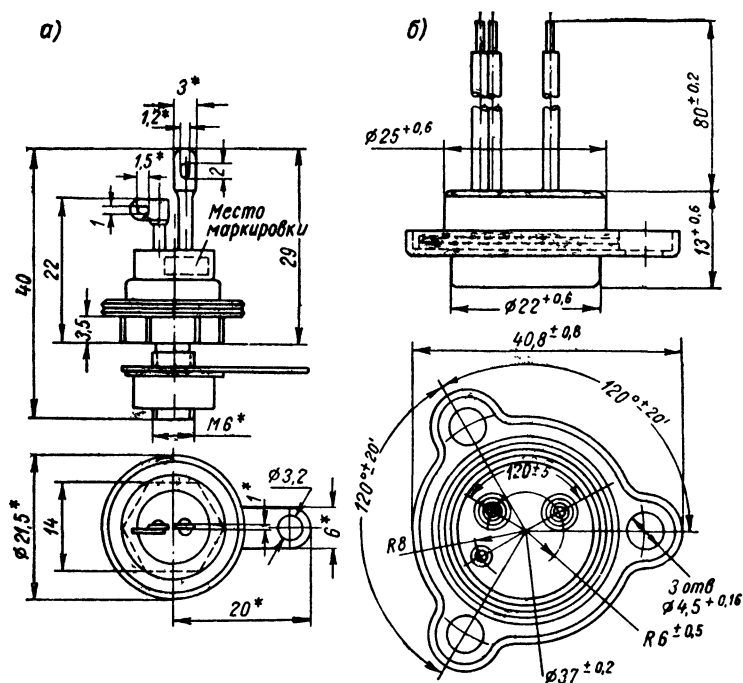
Схематическое устройство и габаритные размеры управляемых кремниевых вентилях: а — типа Д235; б — типа Д238.
